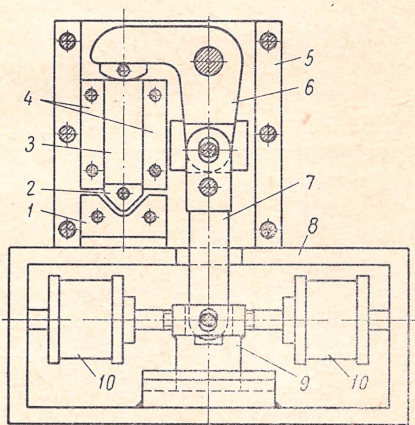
Пневморычажное приспособление для резки профильной угловой стали
